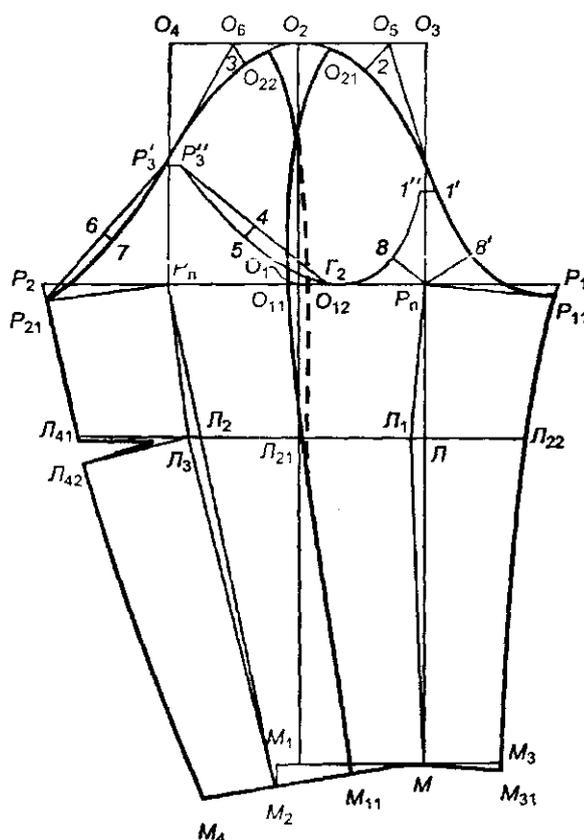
Чертеж двухшовного рукава с верхним и нижним швами
